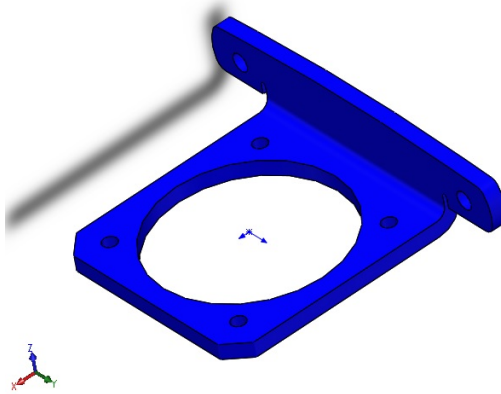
Anclaje motor paso a paso - fondo de la máquina.
